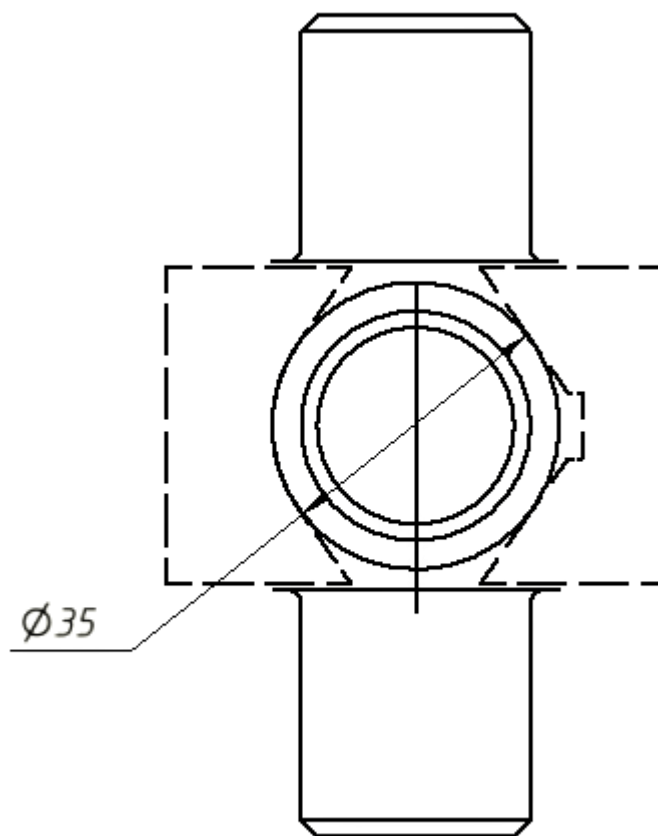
Ескіз деталі (вигляд збоку) та базування з одной сторони деталі в призмах.
